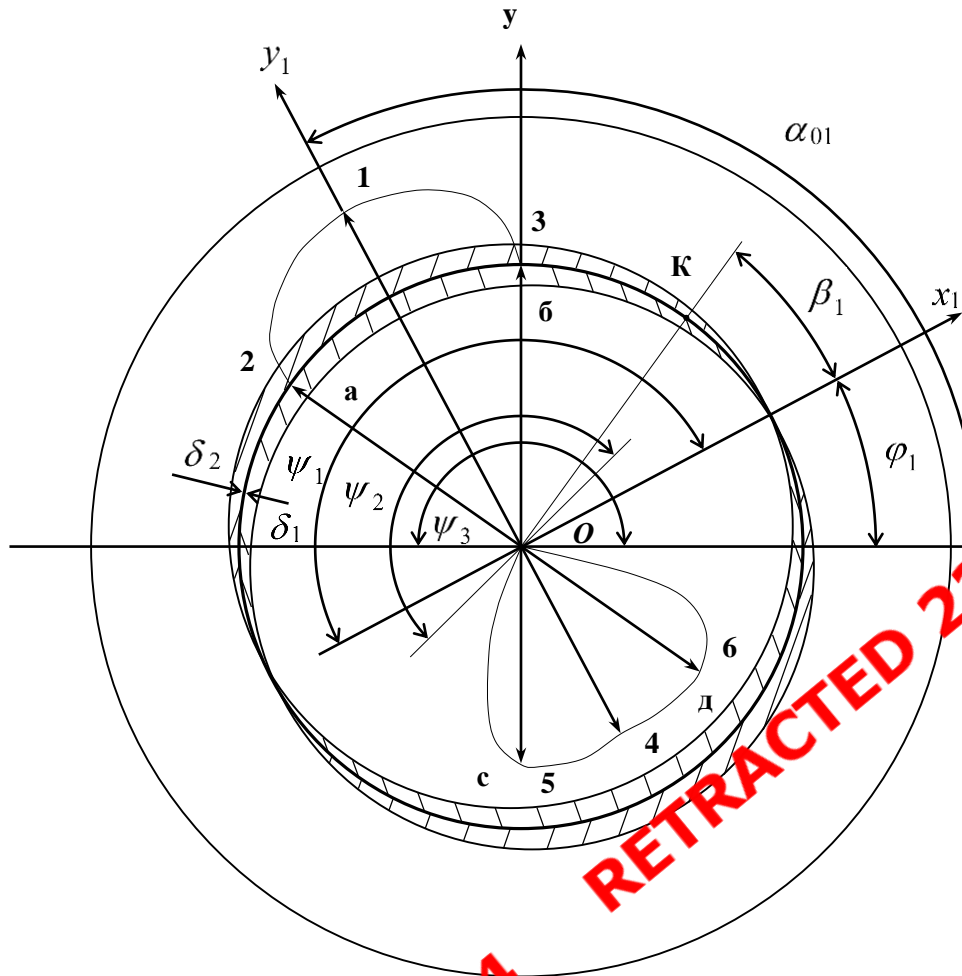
Узел трения, включающий деталь-шейка кривошипа и деталь - головка шатуна
